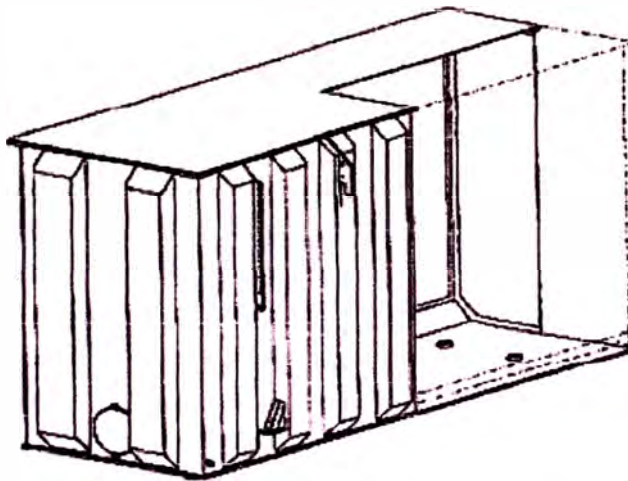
Tanque con refuerzos tipo viga, mostrando los ganchos de elevación y apoyo paragatas
